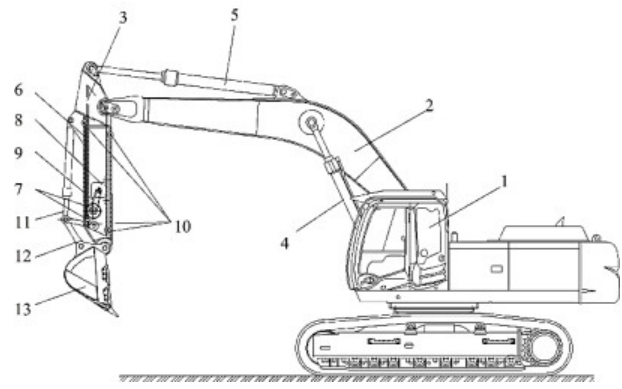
Конструктивна пропозиція патент на корисну модель №101091: 1 – базовий трактор; 2 – стріла; 3 – основна секція телескопічної рукояті; 4, 5, 11 – гідроциліндри; 6 – ТС рукояті; 7 – зубчато-рейковий механізм; 8 – гідромотор; 9 – клинопасова передача; 10 – роликові опорні елементи; 12 – чотириланковий механізм; 13 – ківі
